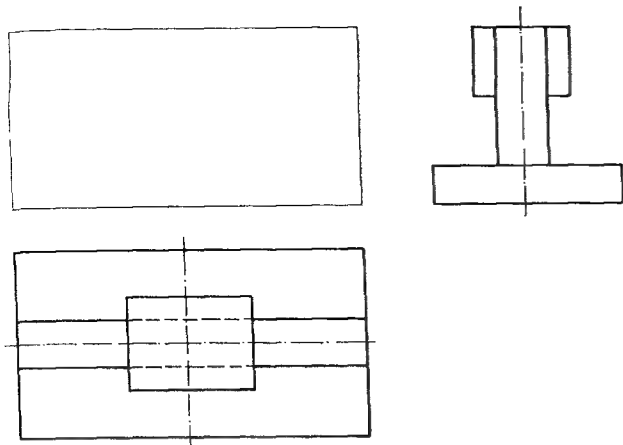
Dibujar el alzado de un objeto representado con planta y perfil.
